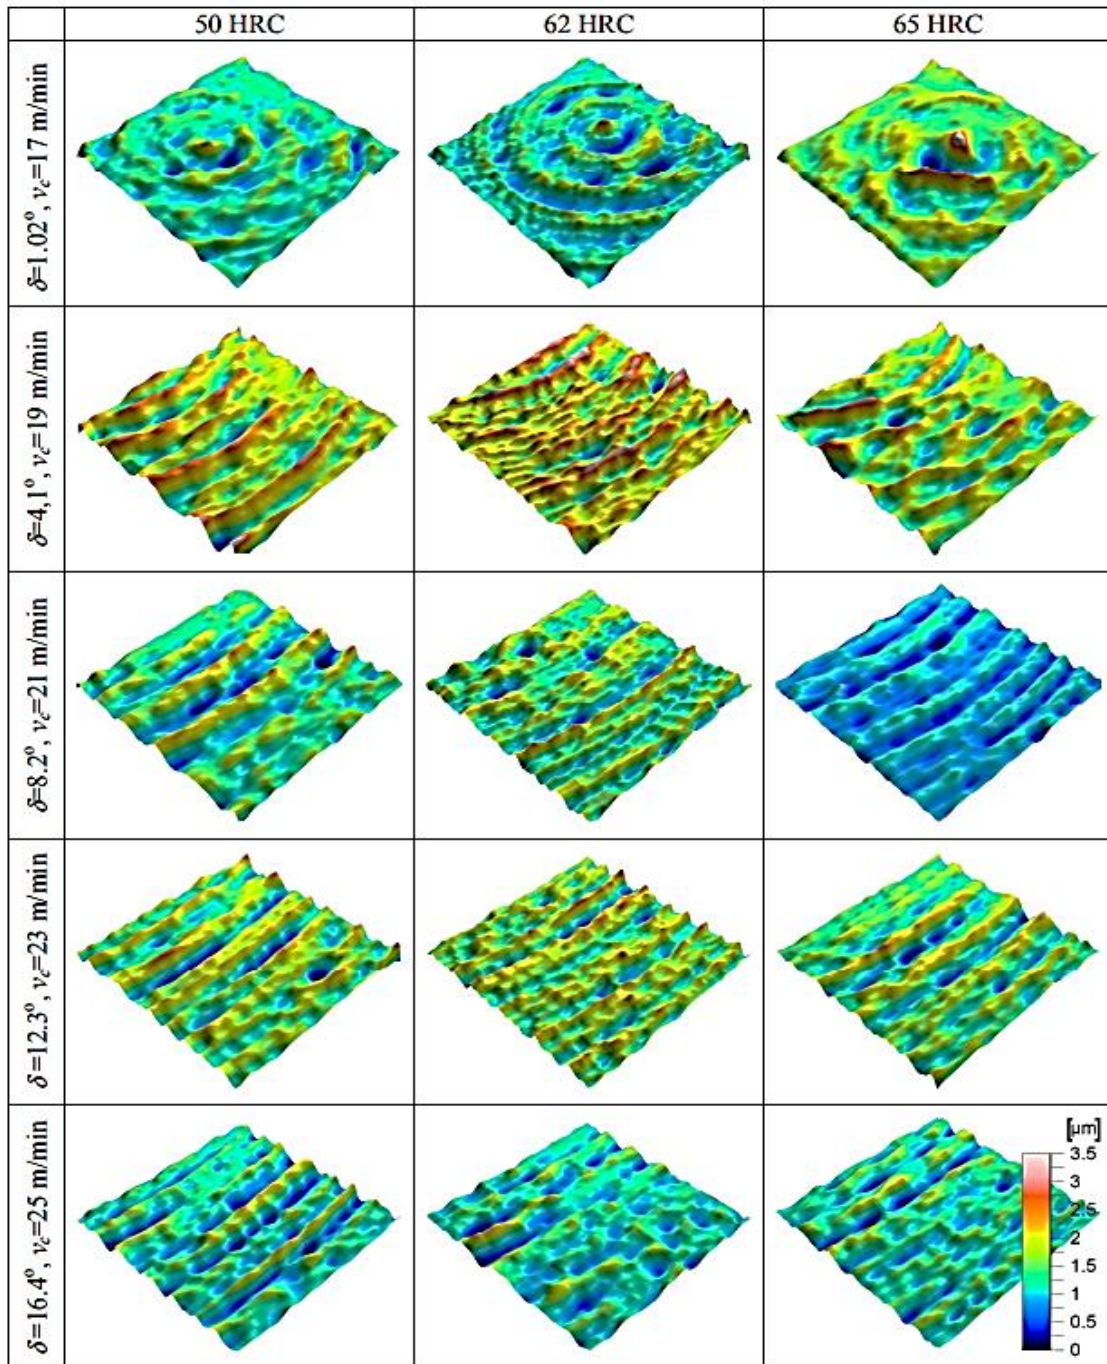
Ізометричні зображення структури поверхні загартованої сталі з різними кутами нахилу інструменту із ПКНБ при подачі $S = 0,016 \text{ мм/зуб}$, глибині різання $t = 0,1 \text{ мм}$) [50]
